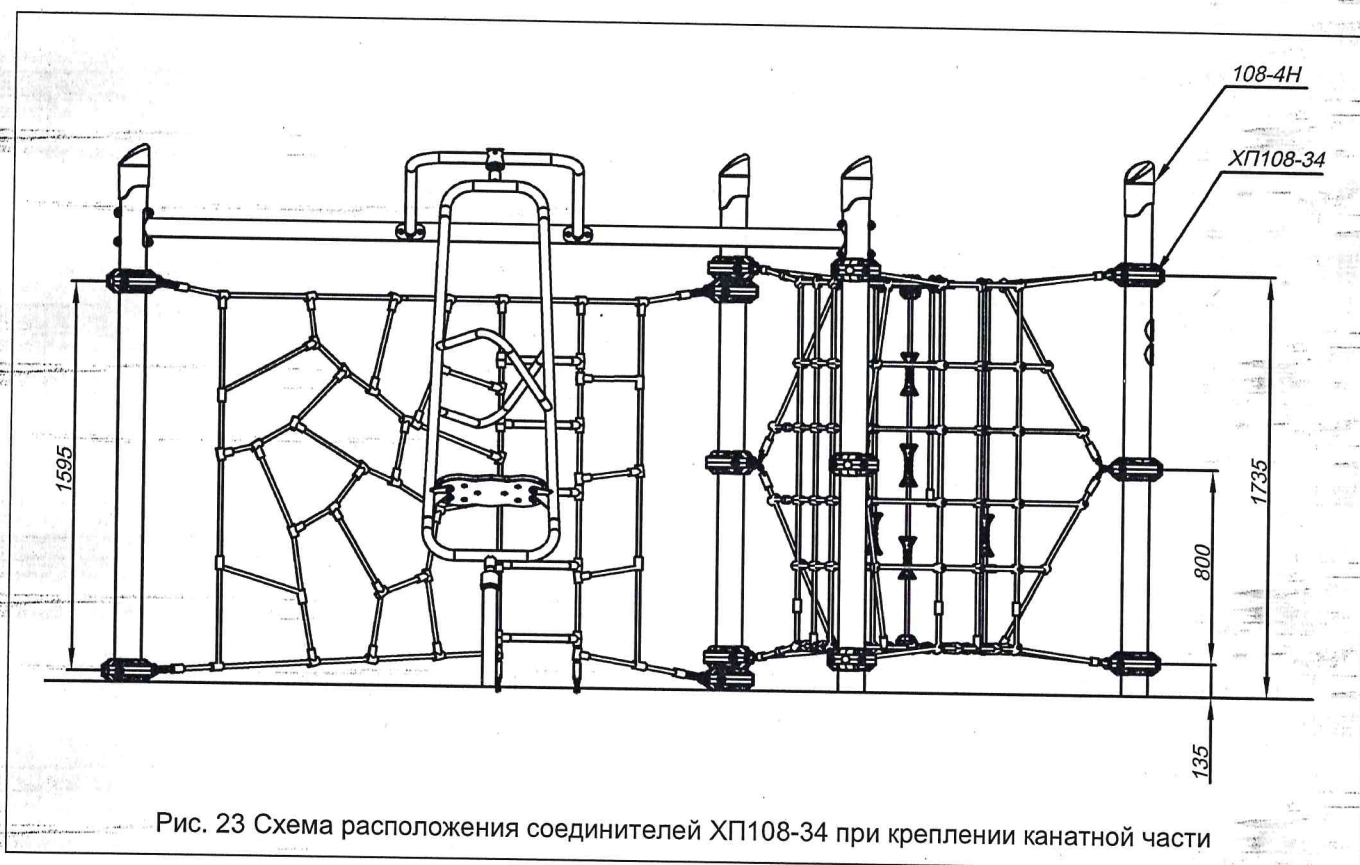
Схема расположения соединителей ХП108-34 при креплении канатной части
